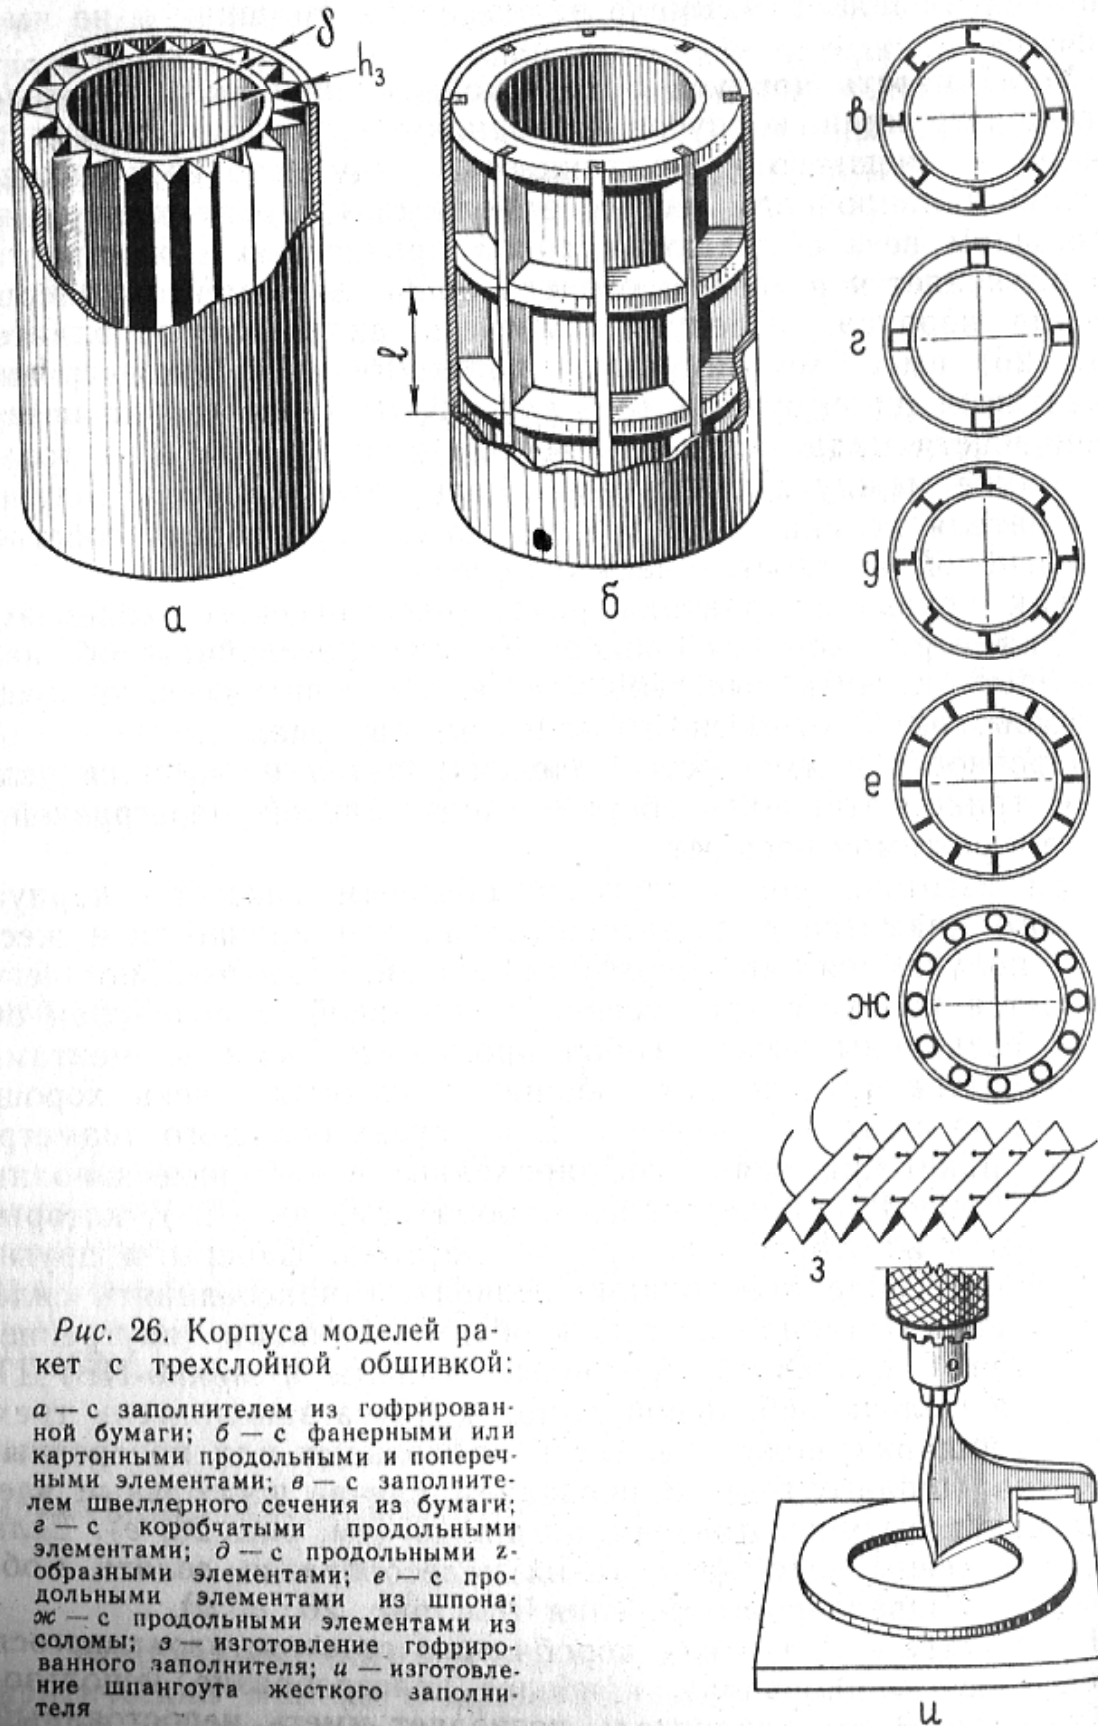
Корпуса моделей ракет с трехслойной обшивкой:
